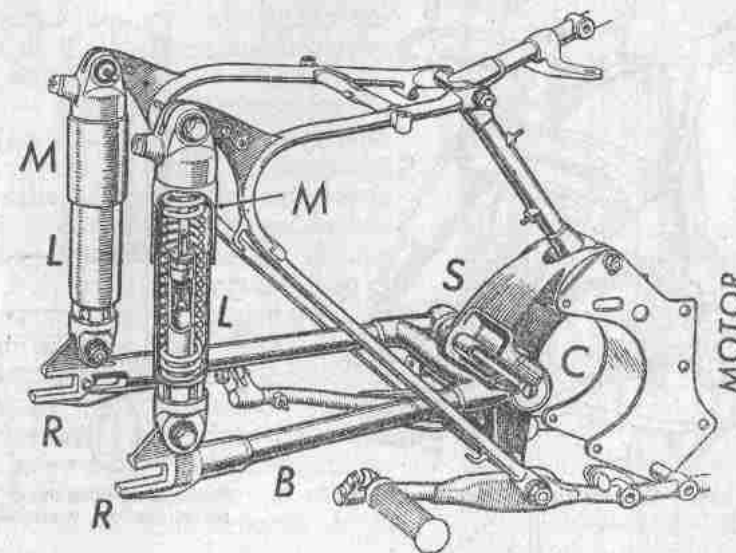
Horquilla *B* oscilante «Teledráulica».
